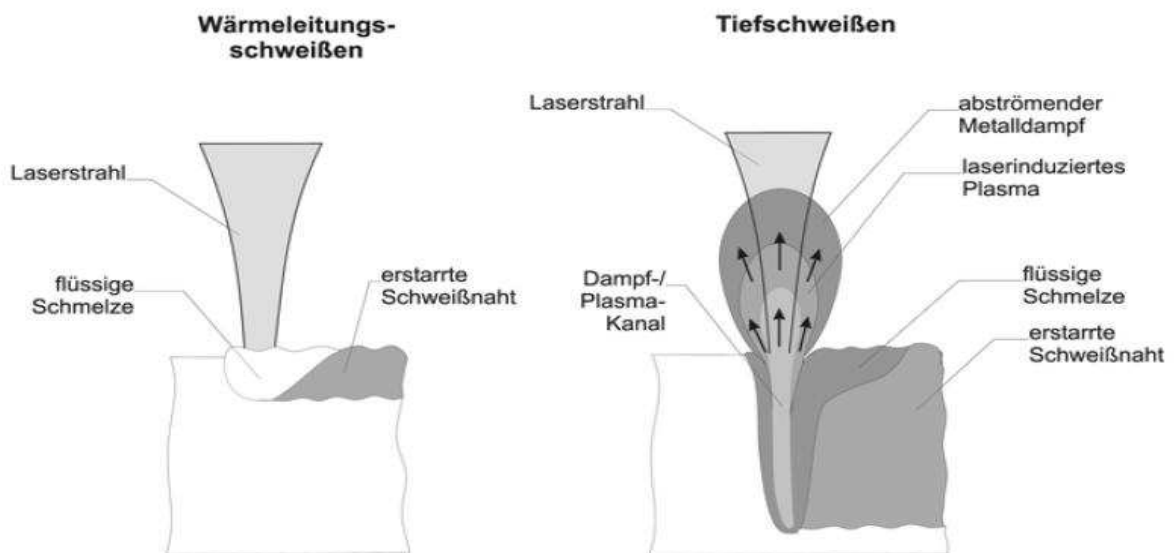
Wärmeleitungs- und Tiefschweißen beim Laserschweißen<sup>[ST01]</sup>
